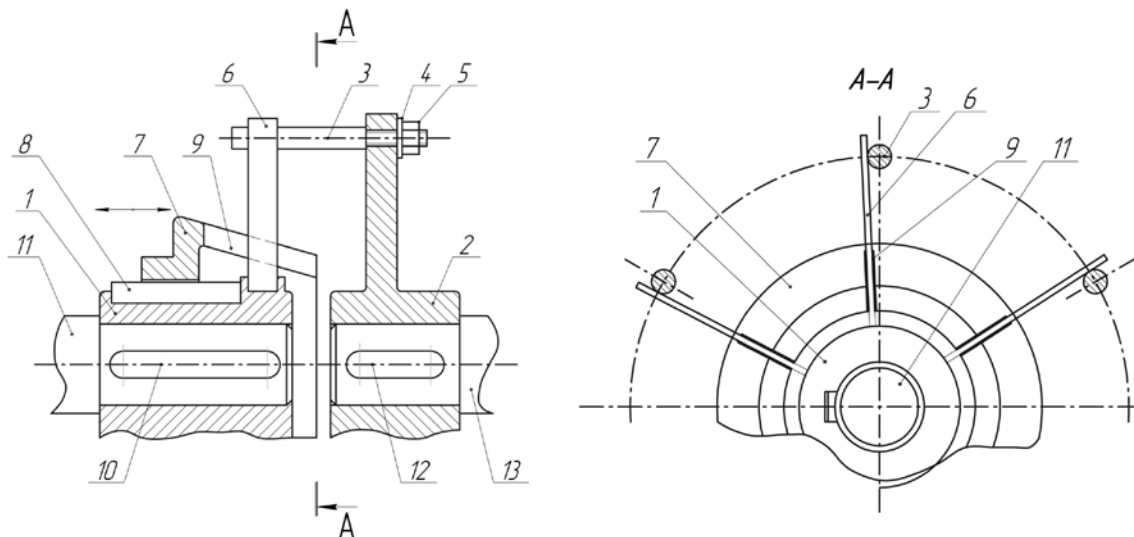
Пружна муфта: 1, 2 – напівмуфти; 3 – пальці; 4 – шайби; 5 – гайки; 6 – плоскі пластинчасті пружини; 7 – конусна втулка; 8 – ковзна шпонка; 9 – радіальні пази; 10 – шпонка; 11 – ведучий вал (вал електродвигуна); 12 – шпонка; 13 – ведений вал (ведучий вал блоку механічних передач)
